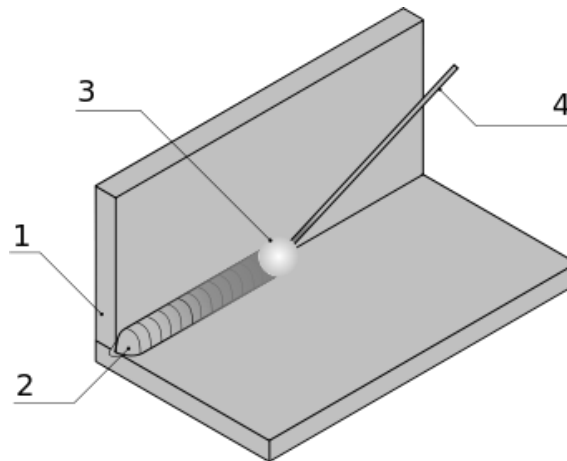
Componentes de un proceso de soldadura por fusión. Tomado de [22].
